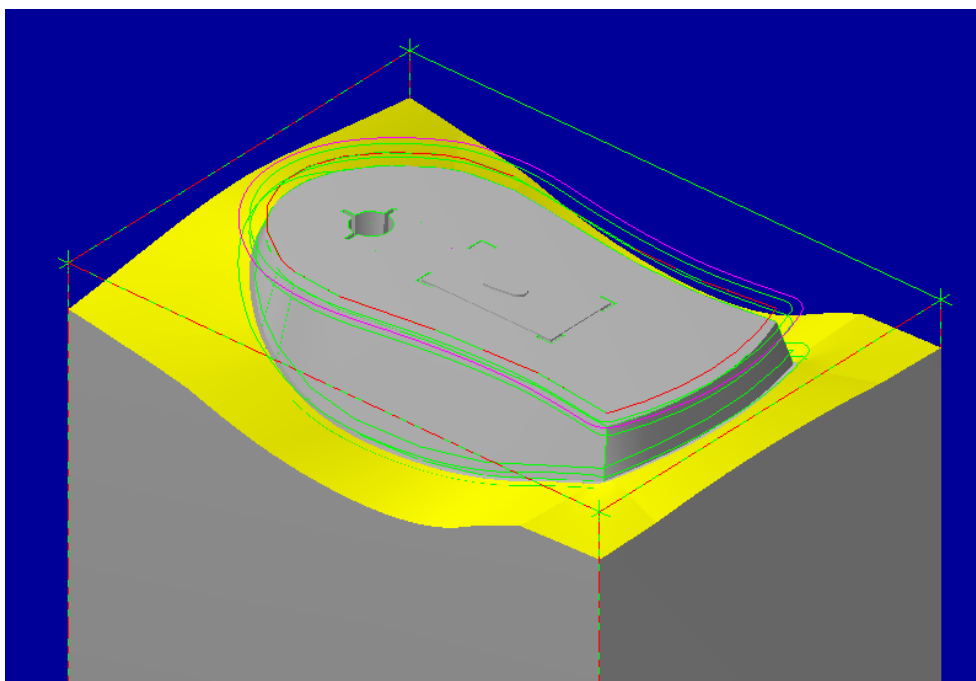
Superfície escolhida para a primeira operação de maquinagem do molde do rato.
